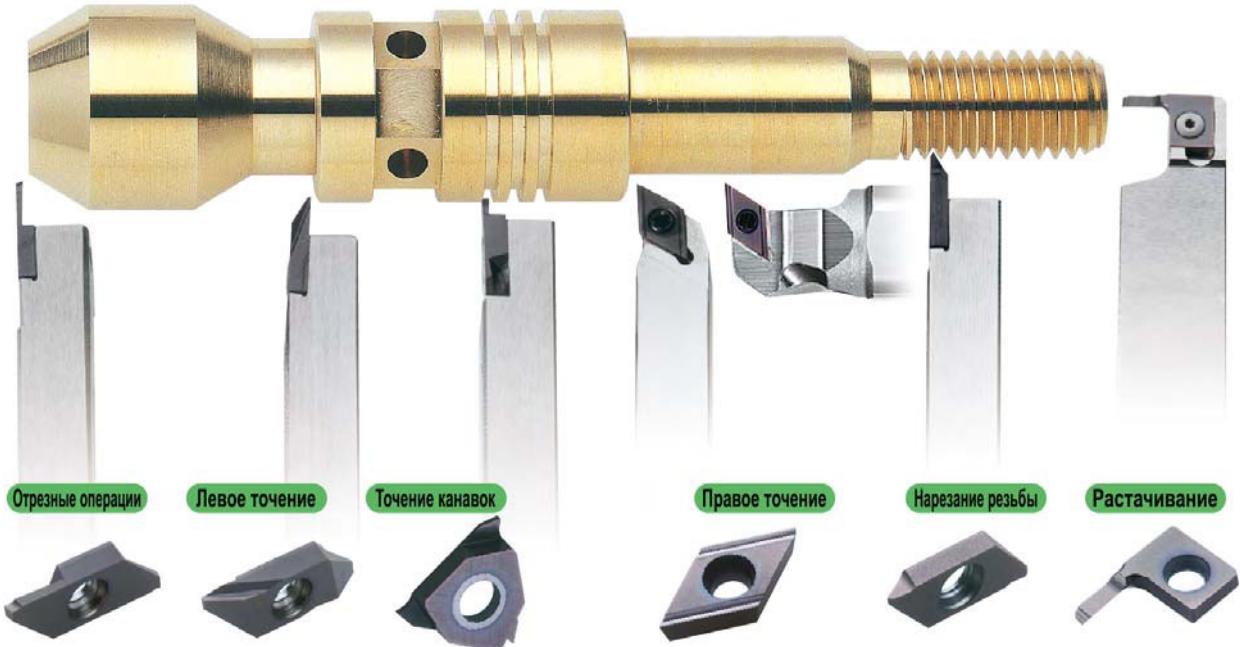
Инструмент для различных видов мелкоразмерной обработки
